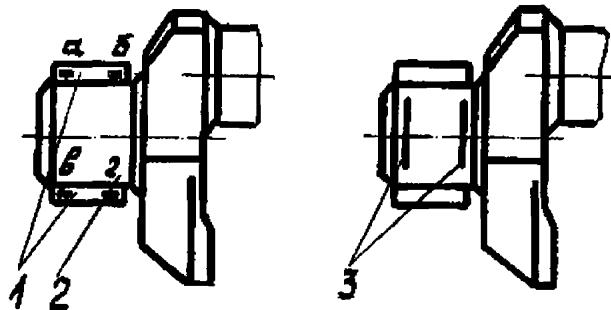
Расположение свинцовых кубиков на вкладышах коренных подшипников и свинцовых проволочек на шейке вала:
